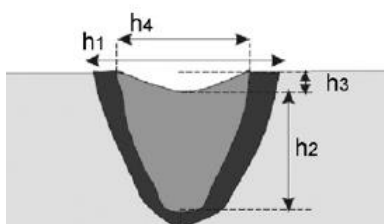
Caracterização dimensional da secção da soldadura.
